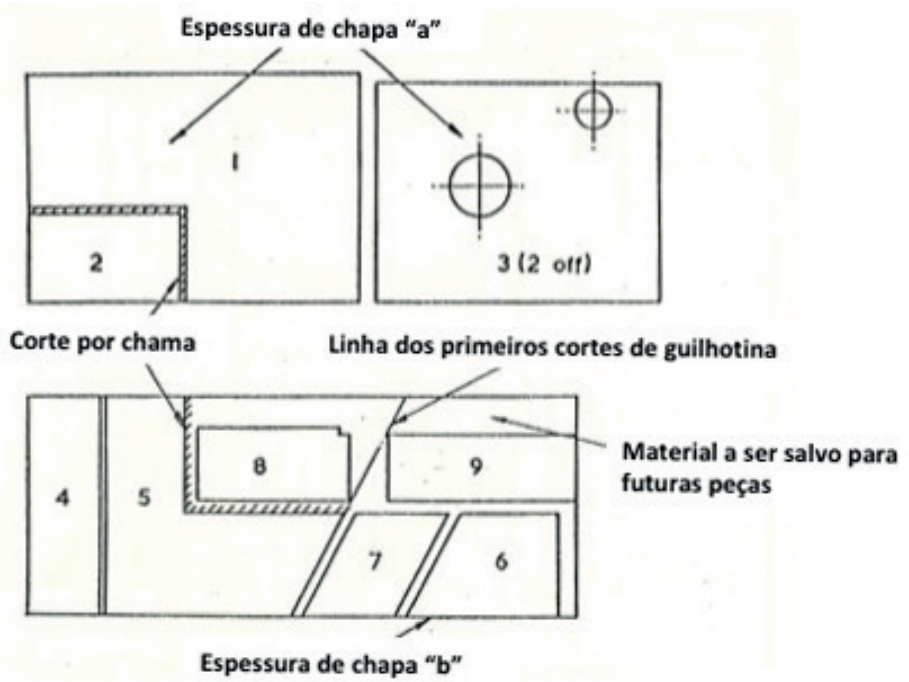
(a) – Layout para placas padrão para caixas de engrenagens soldadas.
